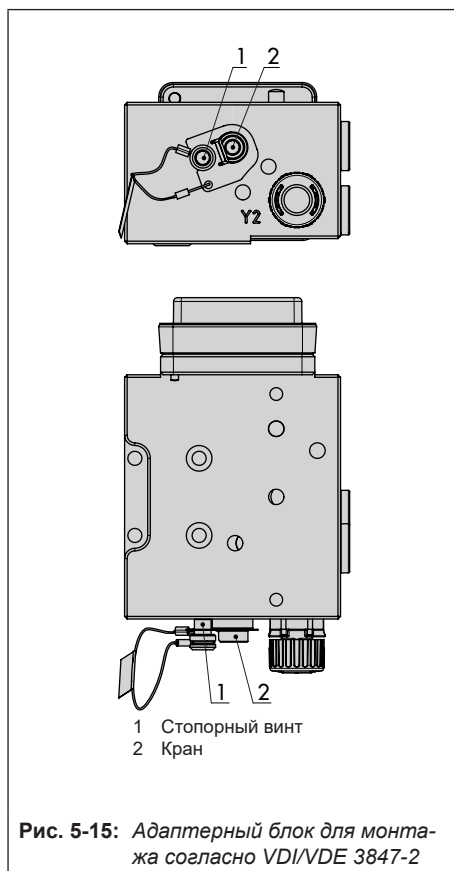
Адаптерный блок для монтажа согласно VDI/VDE 3847-2
